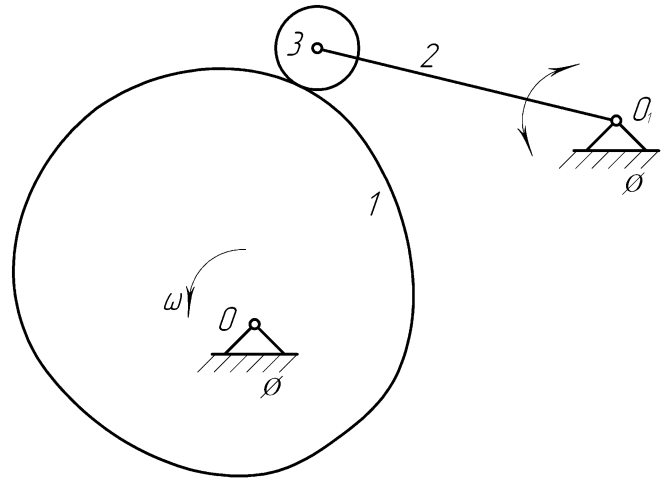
Кулачковий механізм з коливним рухом штовхача
